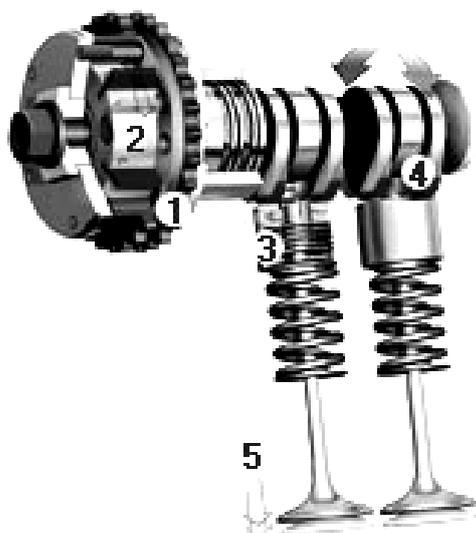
Система изменения фаз газораспределения VarioCAM Plus двигателя Porsche: 1 – зубчатое колесо для привода цепью от коленчатого вала; 2 – муфта переключения фаз; 3 – гидравлический толкатель клапана; 4 – кулачок распределительного вала, изменяющий высоту подъема; 5 – диапазон изменения хода клапанов
